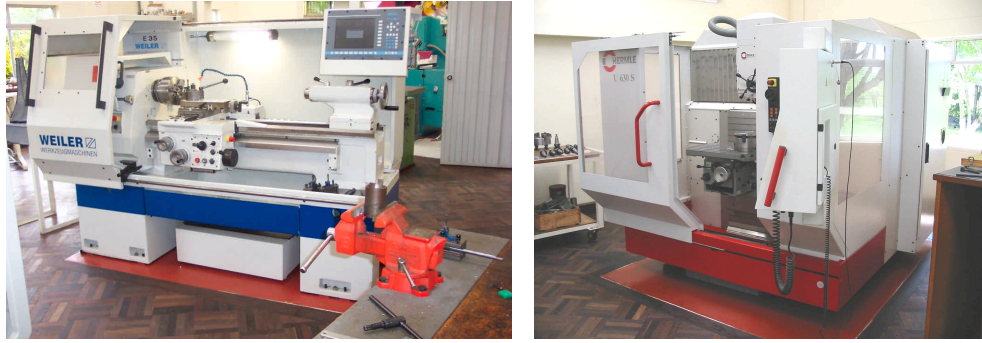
Torno CNC y Centro de Mecanizado de la CIC.
